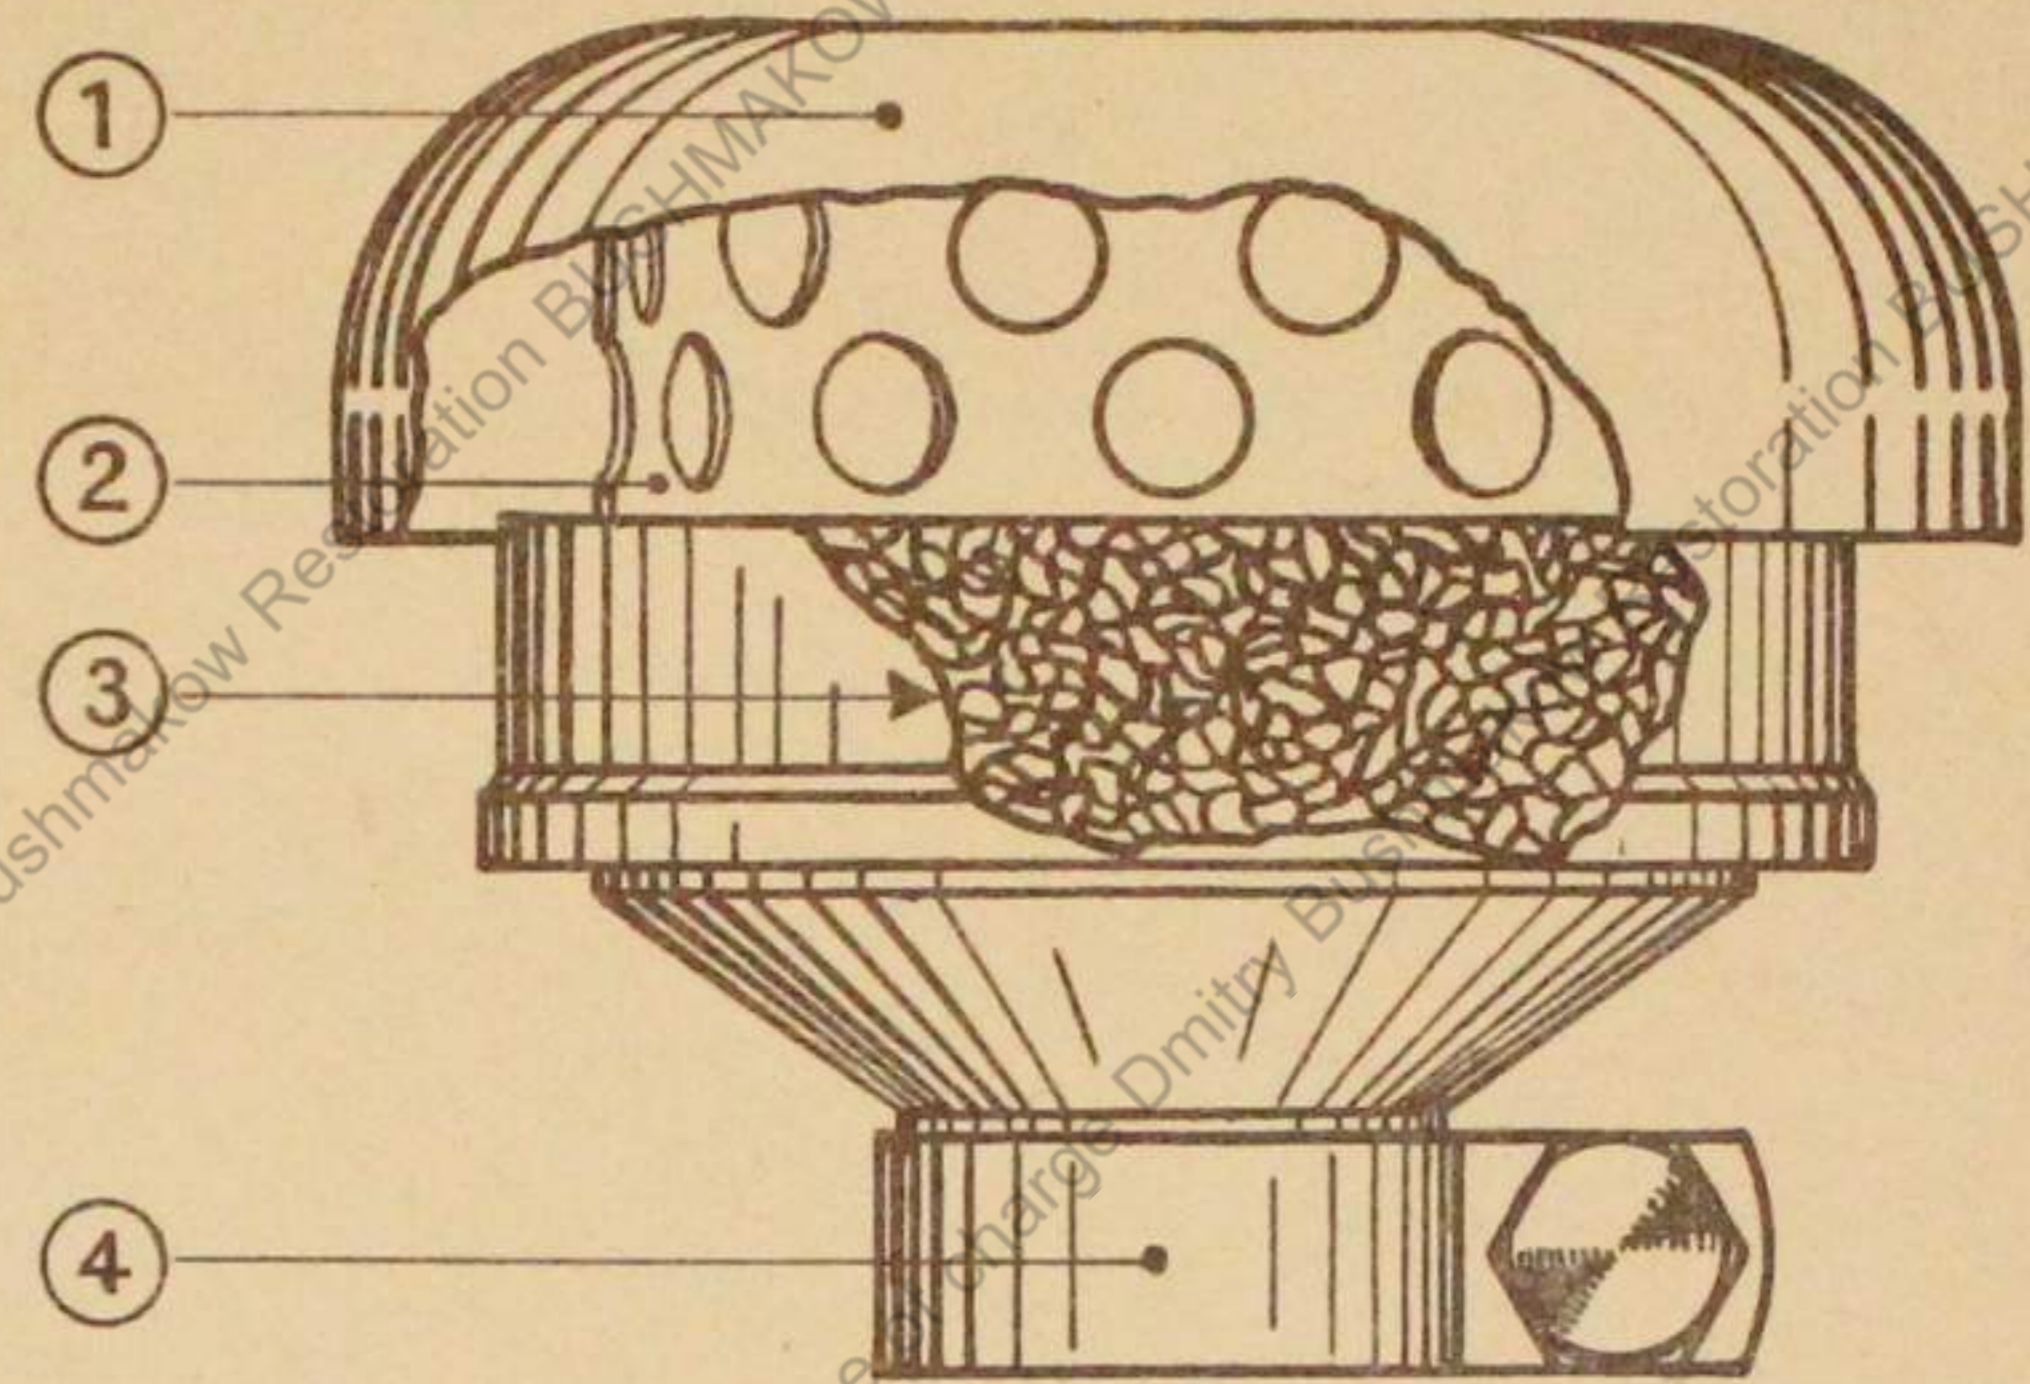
Entlüfter für Wechsel- und Zwischengetriebe
